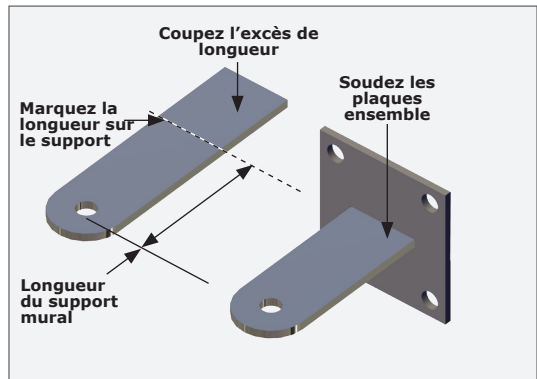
COUPER ET SOUDER LE SUPPORT MURAL
